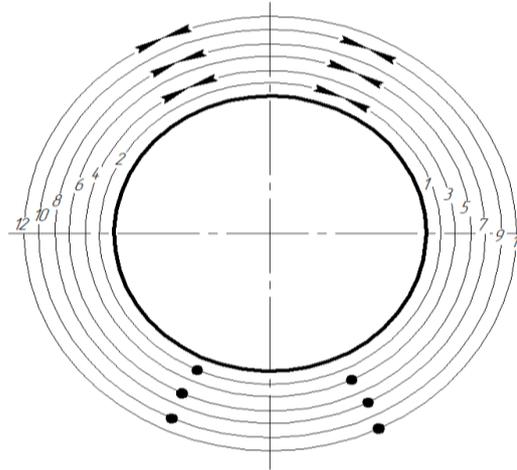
Порядок наложения слоев шва при ручной дуговой сварке: 1-12 – последовательность наложения участков
